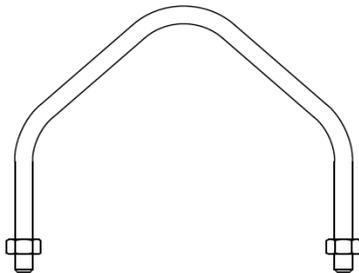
Монтажный кронштейн для трубного монтажа.
